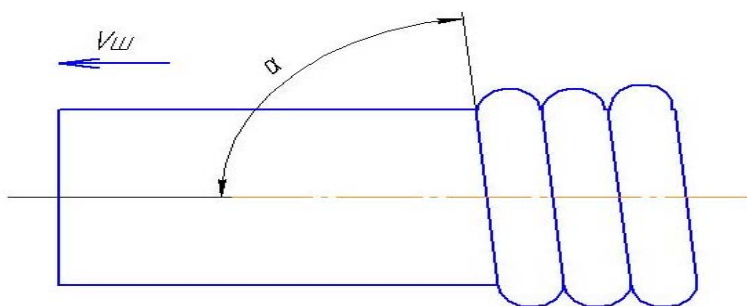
Схема расположения электрода по отношению к наплавляемой детали:
